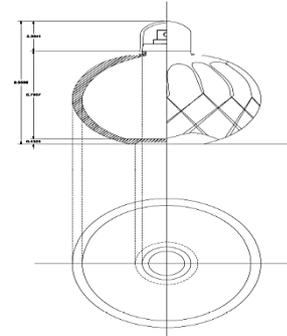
مسقط رأسي وأفقي وقطاع للفكرة التصميمية الثامنة
